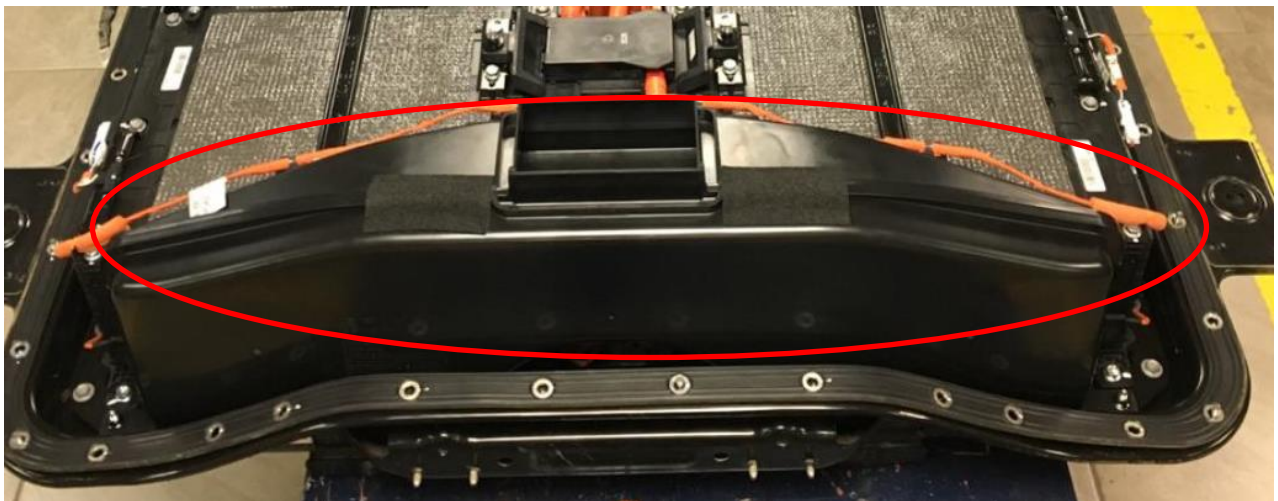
Conducto del sistema de refrigeración. Fuente: Autores.
